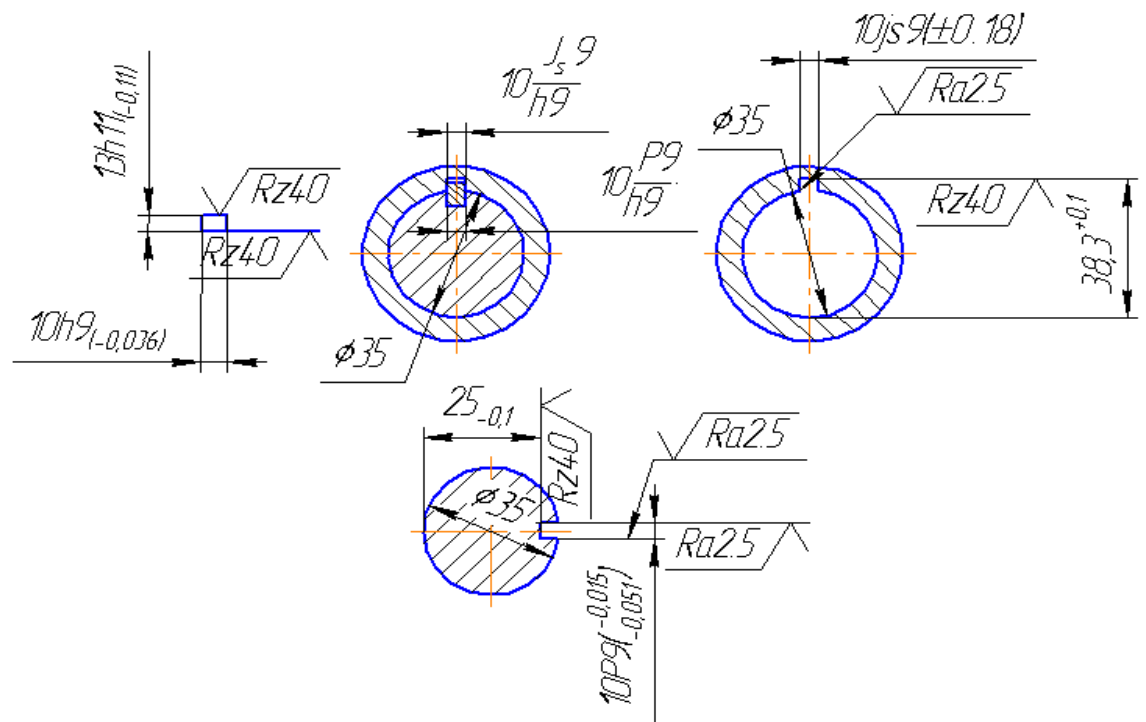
Эскизы шпоночного соединения в сборе и его деталей.
